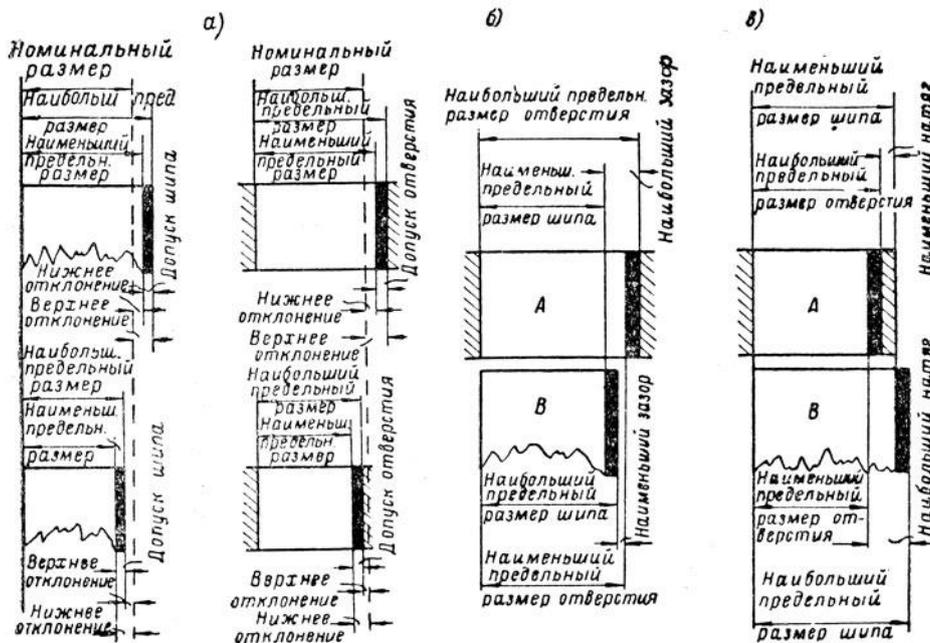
Допуски и посадки: а - наибольший и наименьший предельные размеры; б - зазоры; в - натяги: А - отверстие; В - шип
